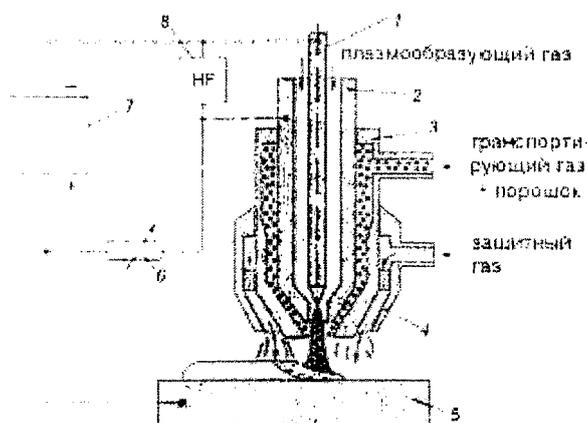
Схема плазменно-порошковой наплавки: 1 – электрод; 2 – плазменное сопло; 3 – фокусирующее сопло; 4 – защитное сопло; 5 – деталь; 6 – балластный реостат; 7 – источник питания; 8 – осциллятор
